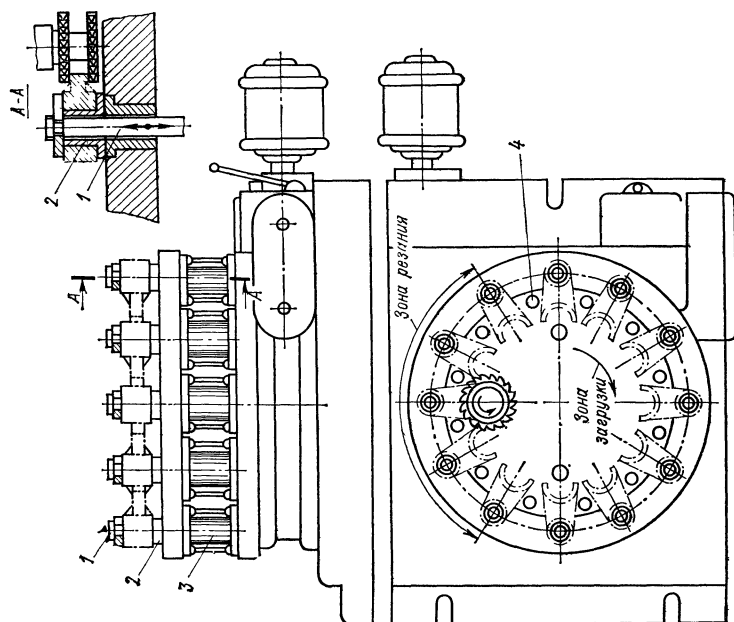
Наладка для непрерывного фрезерования вилок, автоматов чesки закрепляемых с помощью гидравлического зажима
